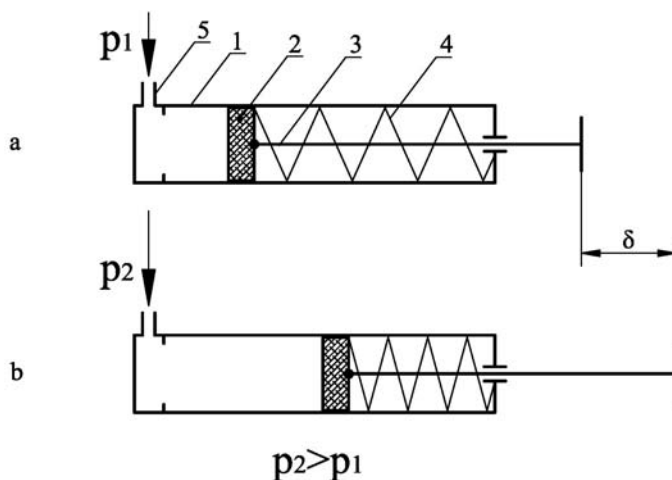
Servomotor pneumatic de tip cilindru cu piston cu simplu efect; 1 – cilindru; 2 – piston; 3 – tijă de acționare; 4 – resort elastic; 5 – racord pentru aer comprimat.
